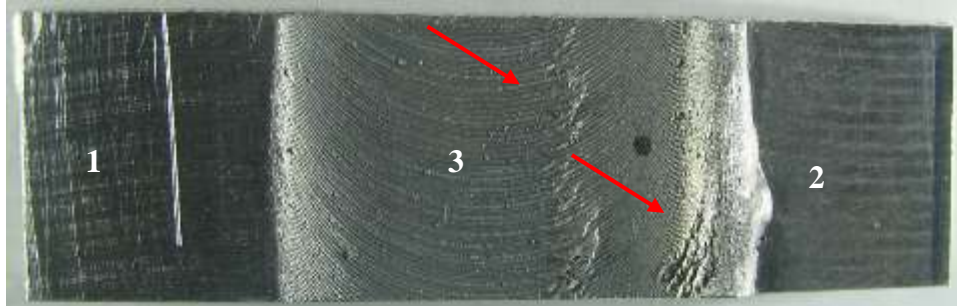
Imagem macroscópica do topo da solda por FSW da junta dissimilar AA2050-T84 com AA7050-T7451.
